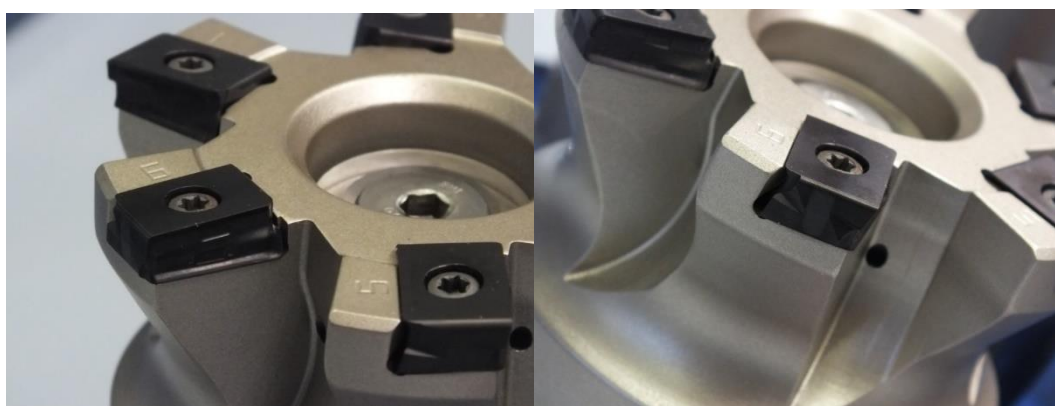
Корпус фрезы с твердосплавными тангенциальными пластинами
